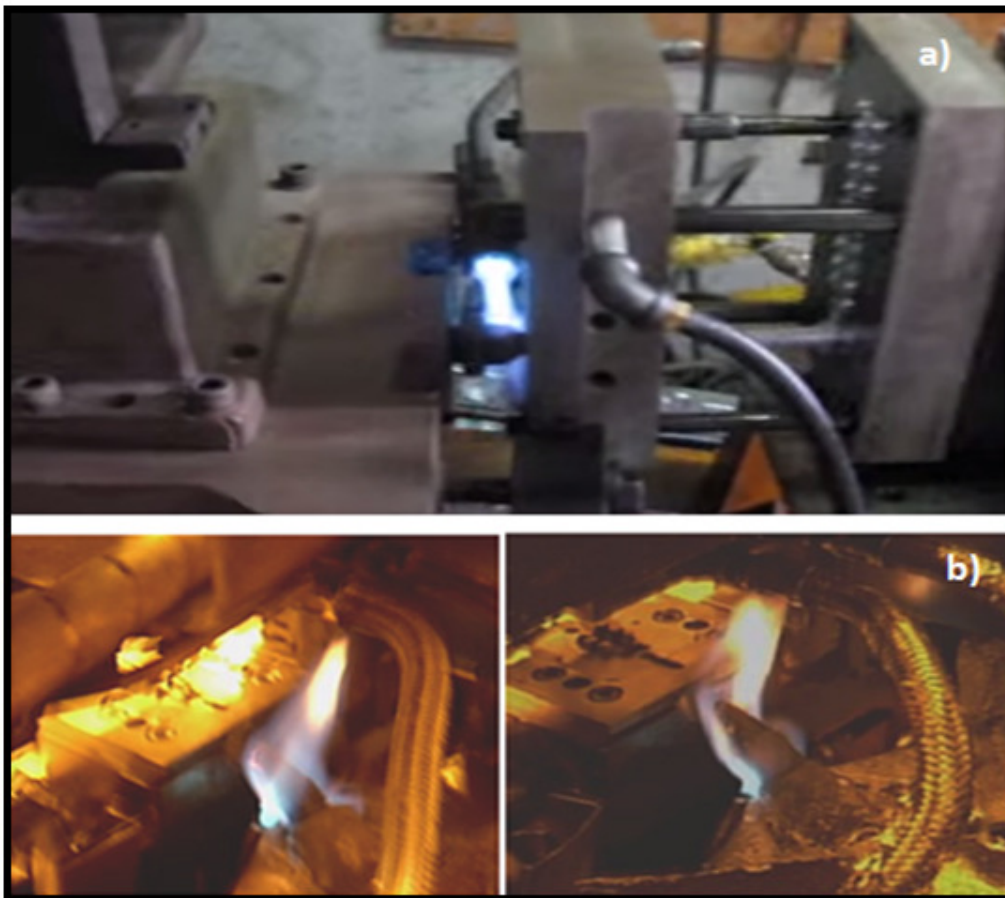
Aquecimento a gás. a) Máquinas de alta pressão, b) Máquinas de baixa pressão.
